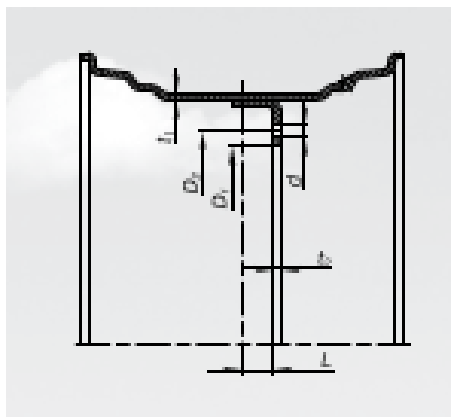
Схематичне зображення штамповано — зварного диска
